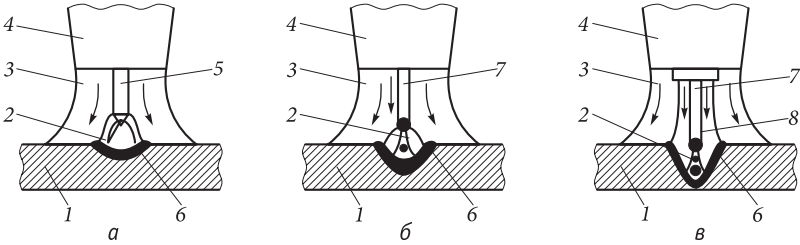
Схемы сварки в защитных газах:
